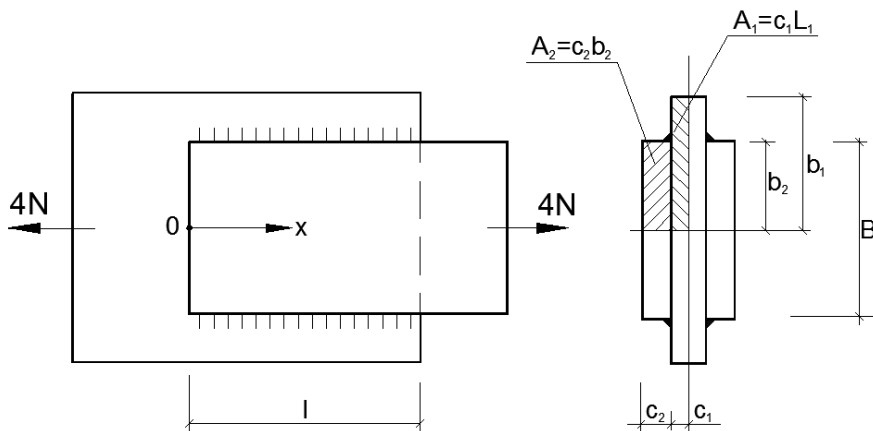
Геометрические параметры сварного соединения с фланговыми швами
